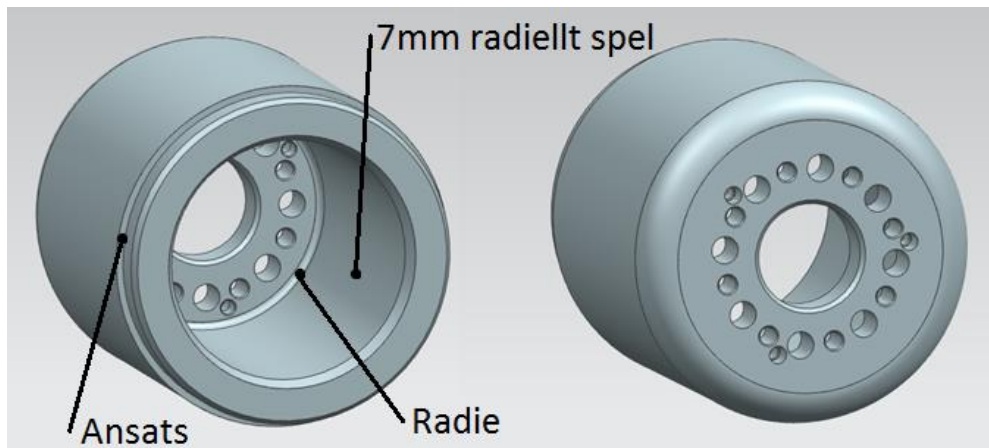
A45 svetsfixturens monteringsfläns, vy till vänster snett framifrån och till höger snett bakifrån.
